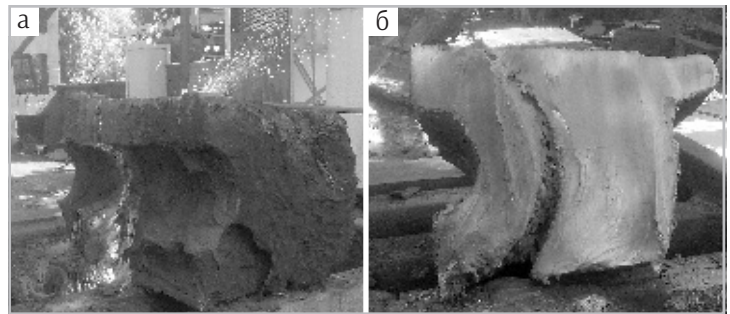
Кислородная резка заготовки сложной формы толщиной 1200 мм: а — с большим расслоением по линии реза; б — поверхность реза заготовки
